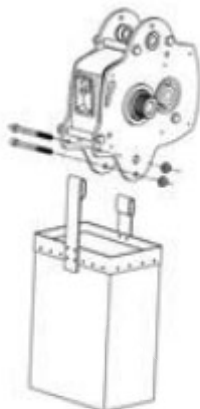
Процесс установки мешка для сбора грузовой цепи
